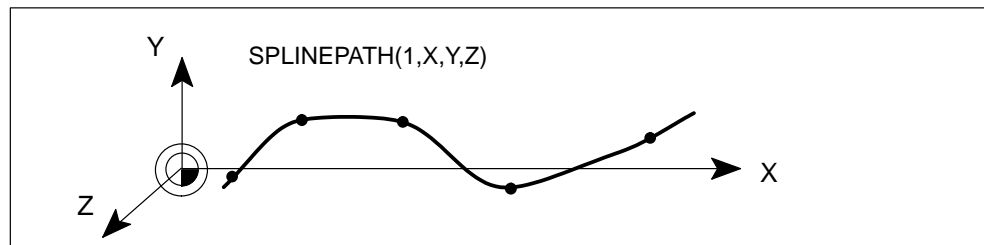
Spline-Verbund, z. B. mit drei Bahnachsen
